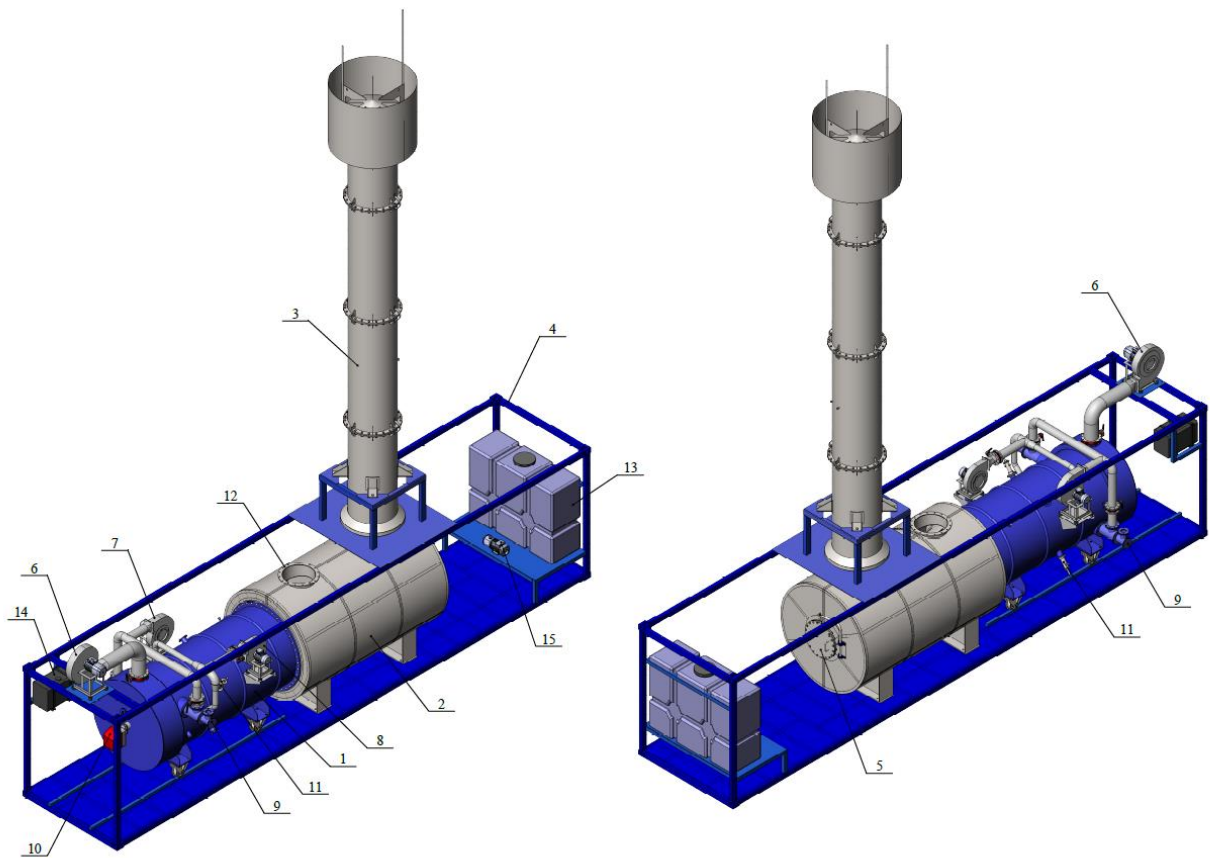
Блочный комплекс. Внешний вид и габаритные размеры
